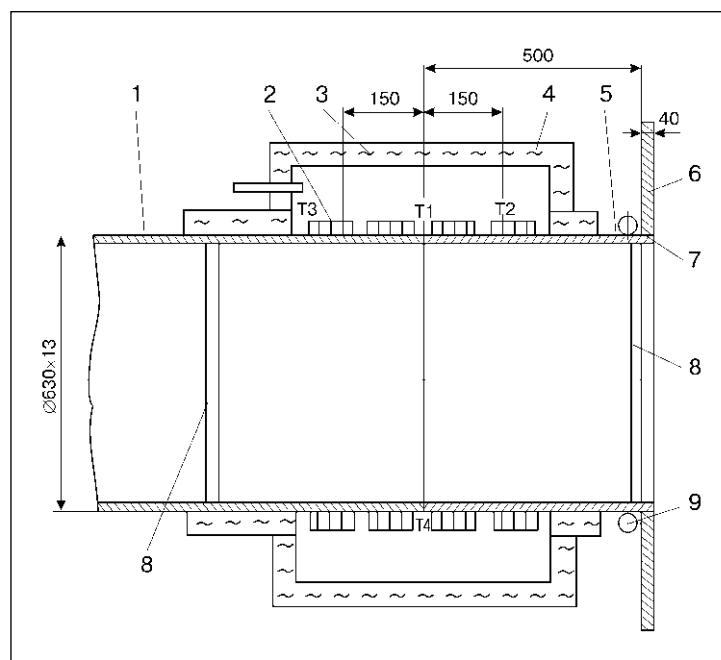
Схема проведения термообработки сварного соединения трубы диаметром 30 мм натриевого водопровода с патрубком теплообменника: 1 — труба; 2 — пояса электронагревателей ГПЭСА; 3 — защитный кожух; 4 — теплоизоляция; 5 — патрубок теплообменника; 6 — теплообменник; 7 — сварной шов; 8 — отражательные экраны; 9 — трубка для подачи воздуха; Т1—Т5 — места установки термопар
